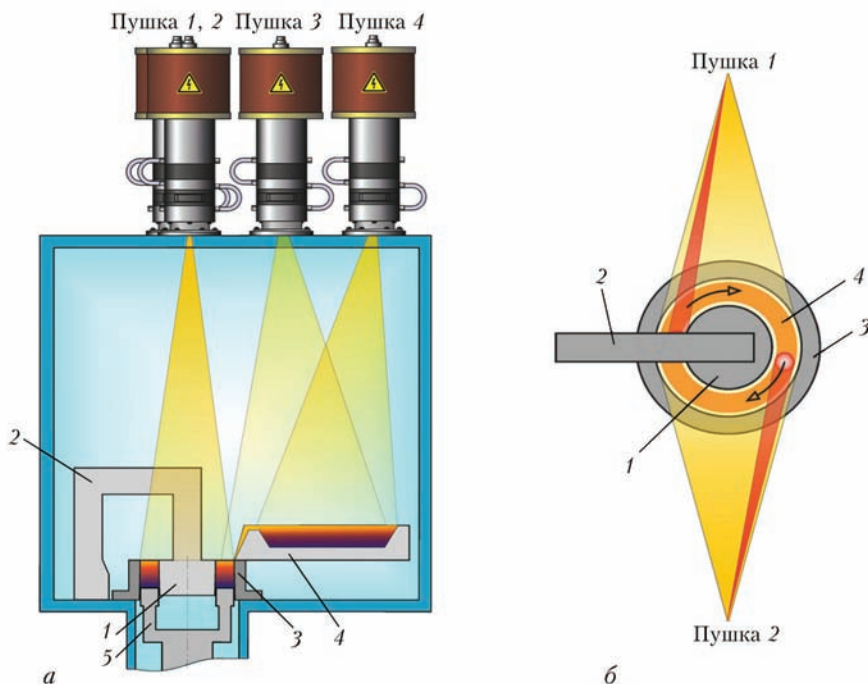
Схемы конструкции кристаллизатора для получения трубчатой заготовки способом ЭЛП (а) и нагрева ванны расплава двумя электронными пушками с развертками лучей в форме полуколец (б, вид сверху): 1 — водоохлаждаемый дорн; 2 — траверса; 3 — водоохлаждаемый тигель; 4 — промежуточная емкость; 5 — водоохлаждаемый шток с затравкой
